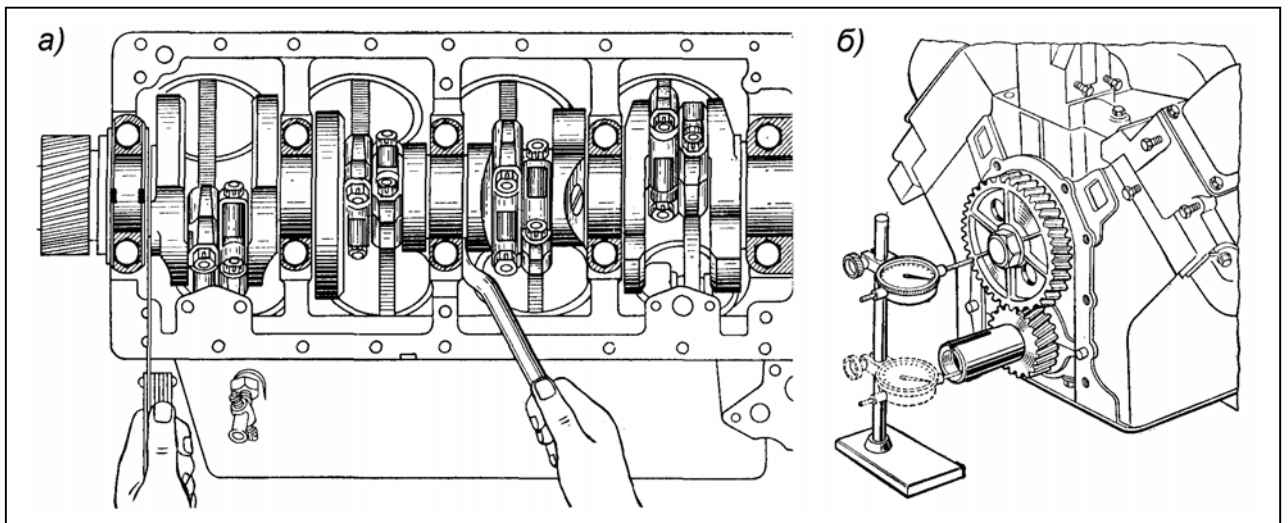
Контроль осевого зазора в упорном подшипнике коленчатого вала:
